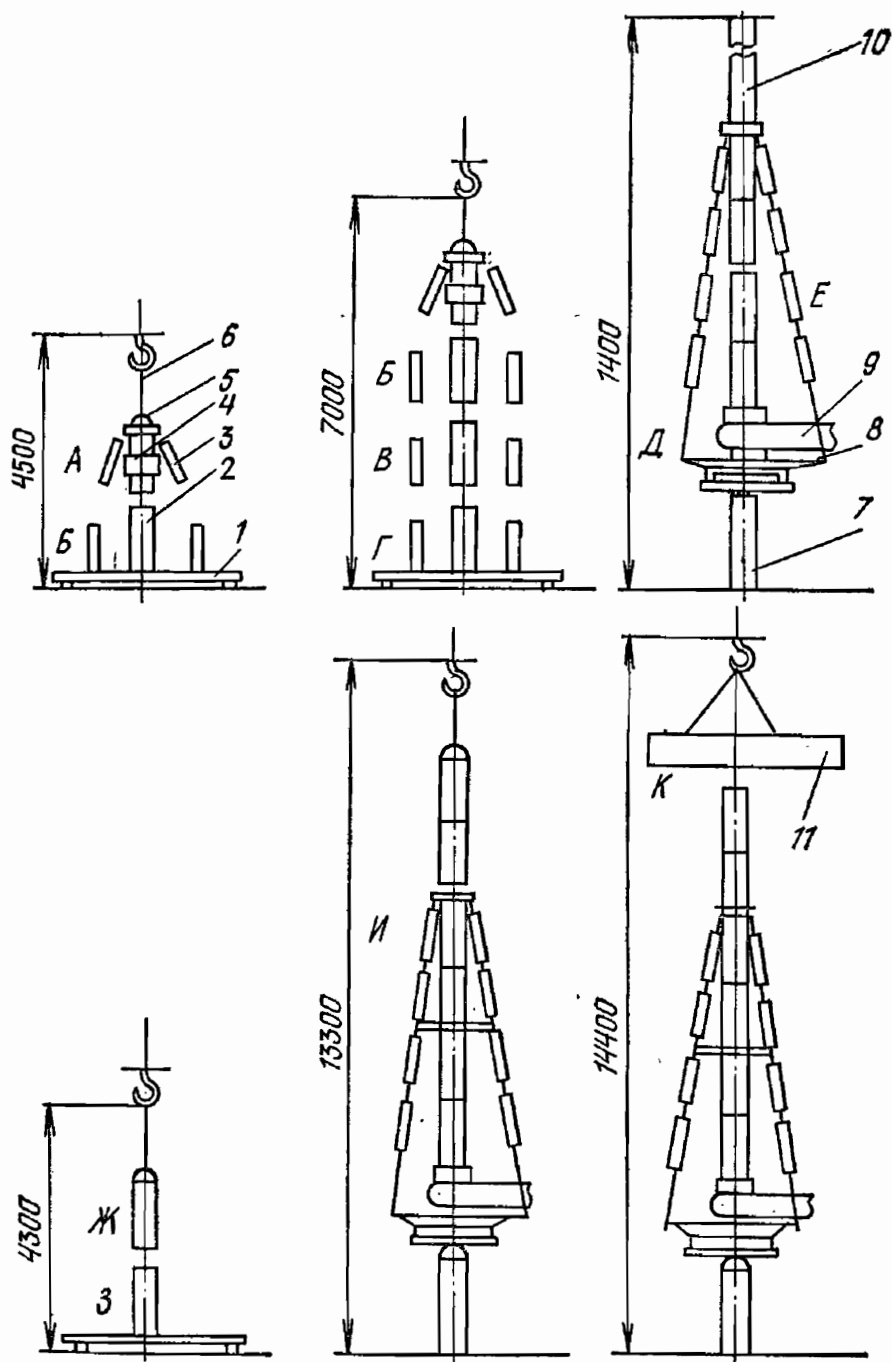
Сборка опорной колонки и установка дугогасительного устройства:
